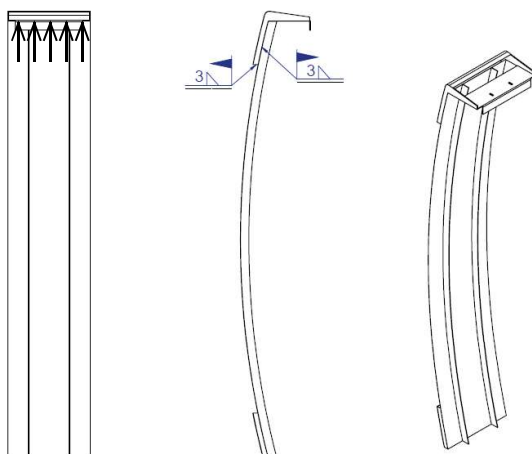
Desarrollo formal. Frontal. Cargas y zona a soldar.
